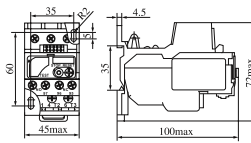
configuração geral TRR2-25 e dimensão da instalação com base de montagem
